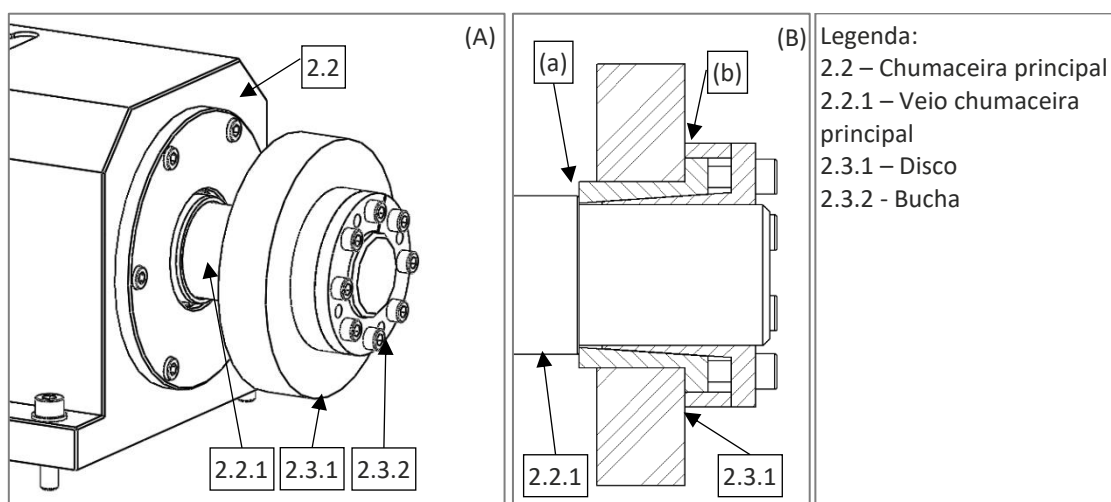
Fixação do disco; (A) vista isométrica; (B) vista de corte
